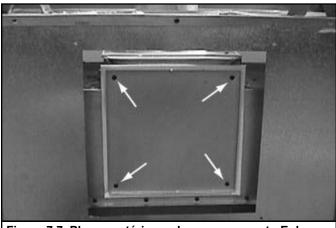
Plaque extérieure de recouvrement - Enlever la plaque
